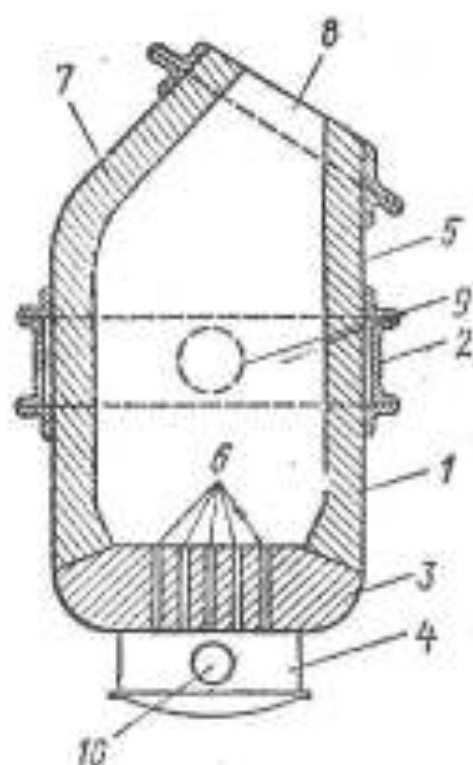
Схема устройства бессемеровского конвертора:
